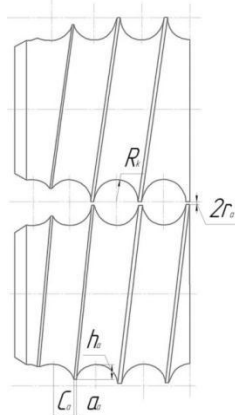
Основные элементы калибровки валков для прокатки шаров
